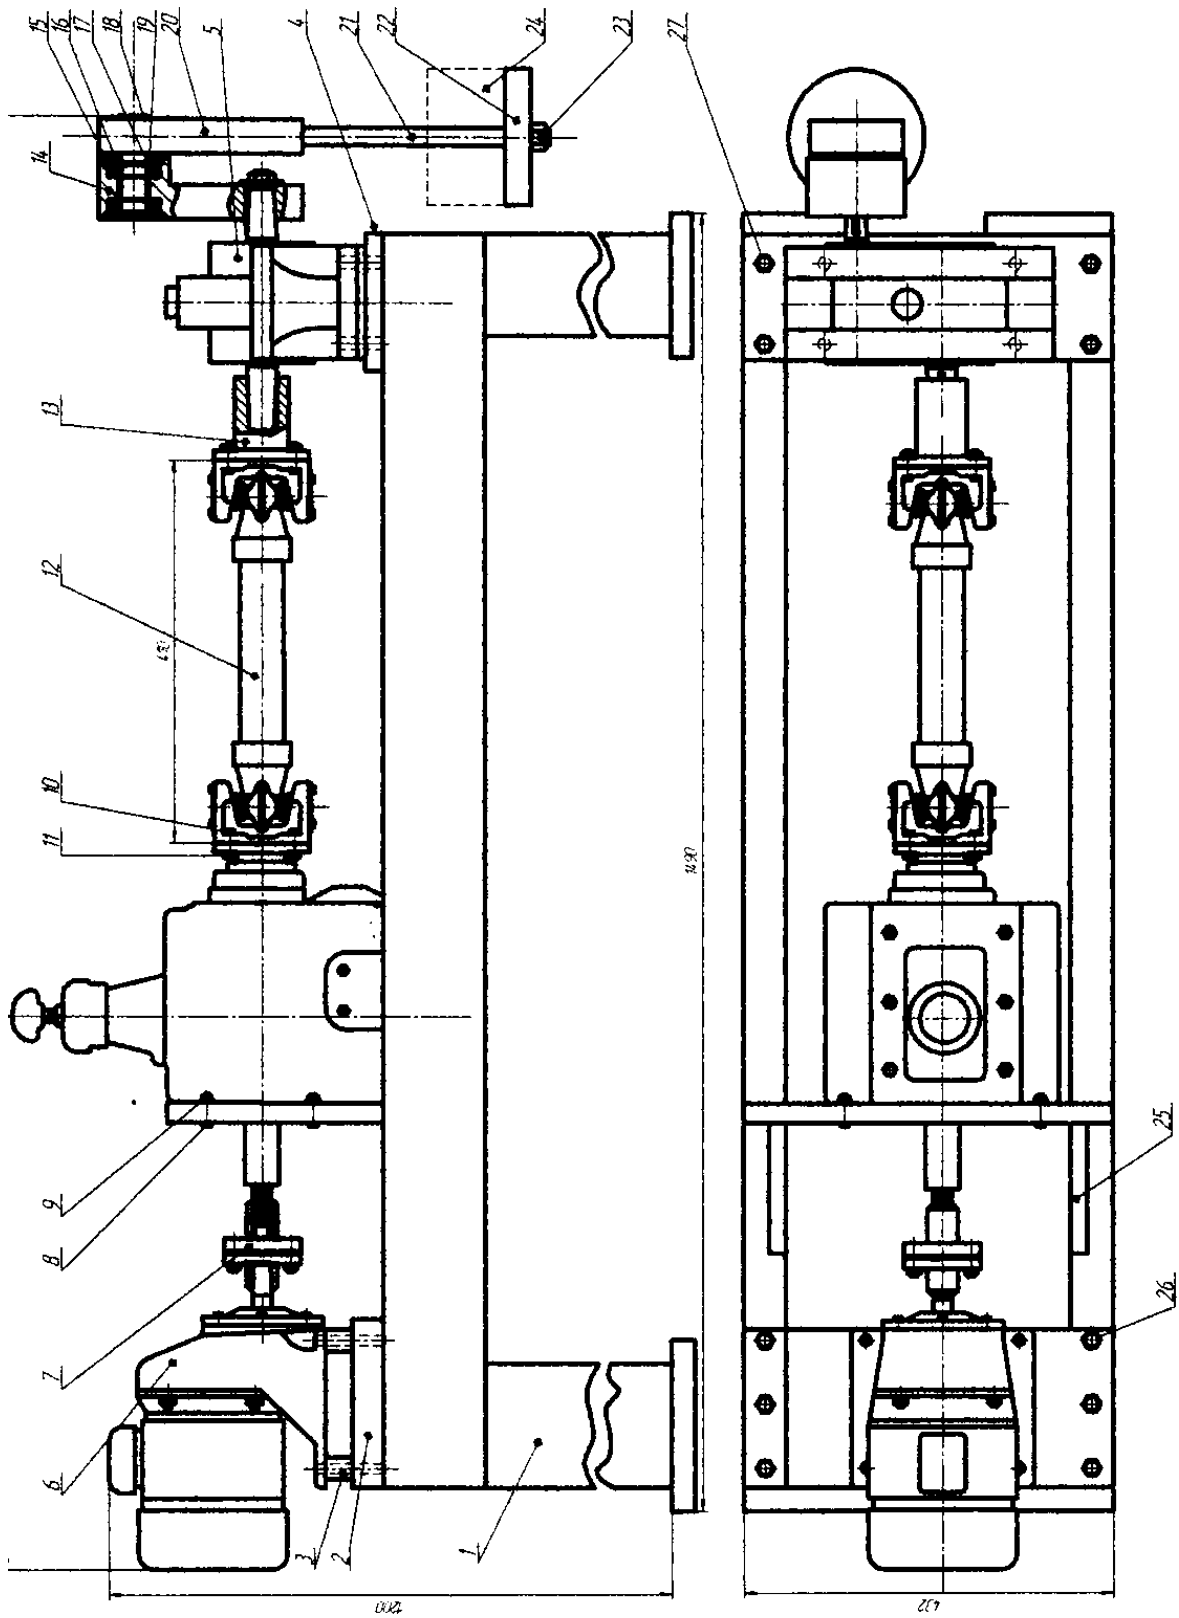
Загальний вигляд пристрою для визначення технічного стану коробок передач
